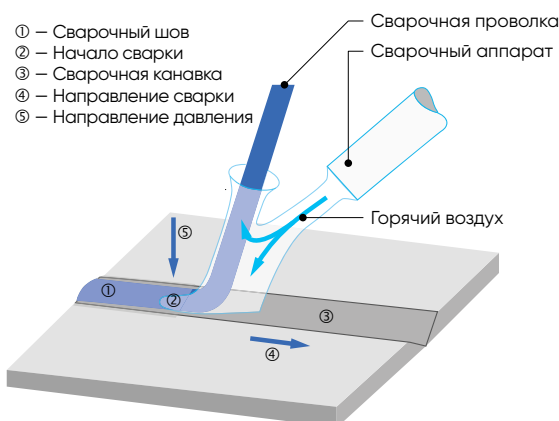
Сварочный аппарат типа WZ
